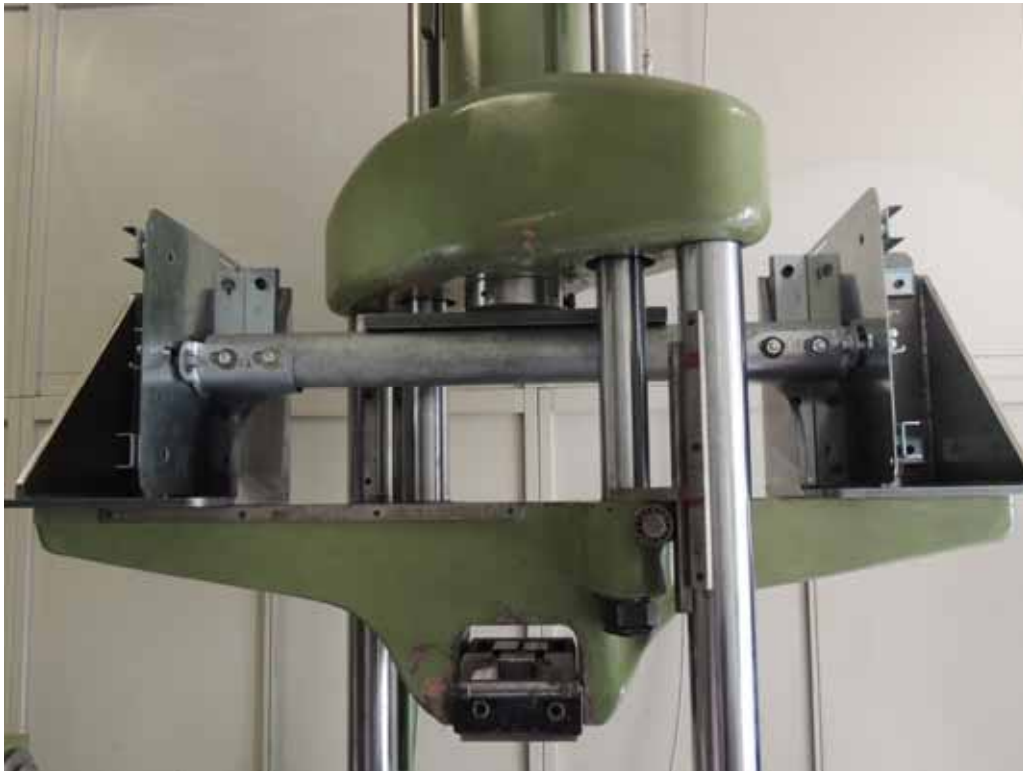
Guida esterna – Albero Ø 76 mm – Inizio prova
